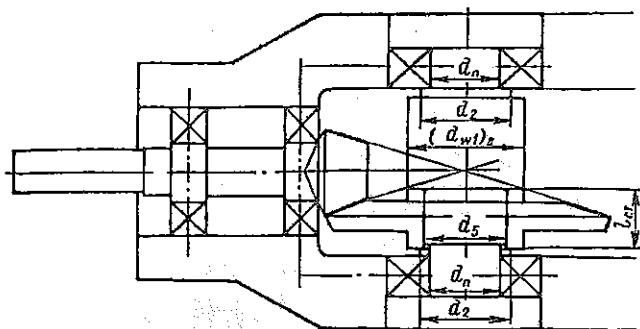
Компонровка промежуточного вала коническо-цилиндрического редуктора
